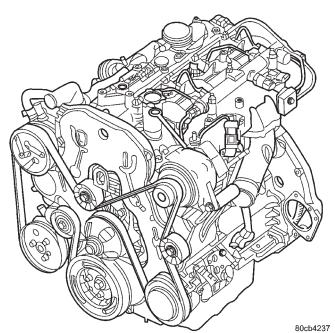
MOTOR 2.5L DIESEL DE TUBO DISTRIBUIDOR COMUN
